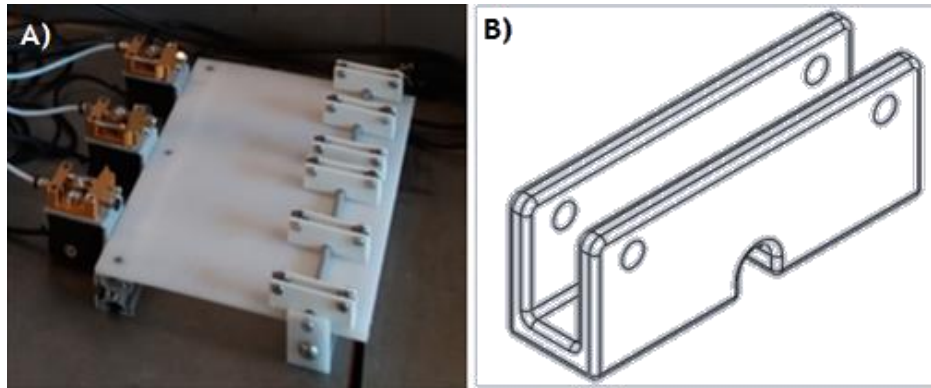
A) Suportes de bobine de filamento e respetiva guia; B) Esboço do desenho CAD para impressão.
